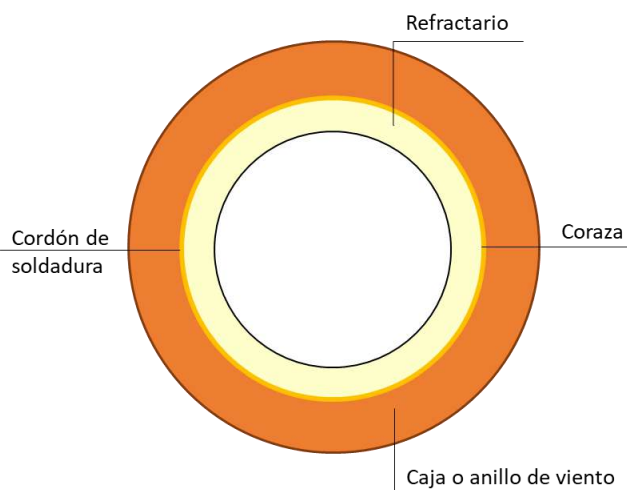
Esquemático con vista de planta del anillo o caja de viento
